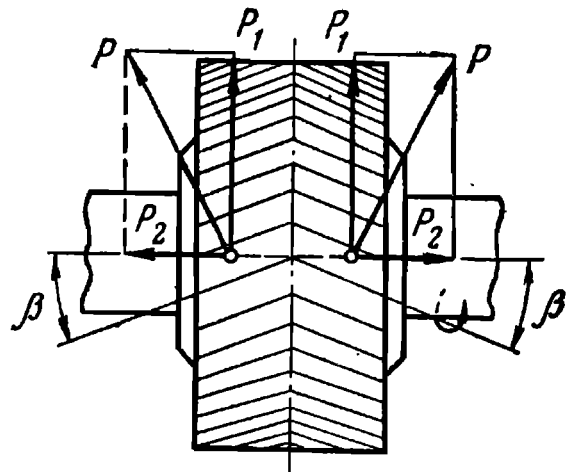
Схема зубчатого колеса с шевронными зубьями
